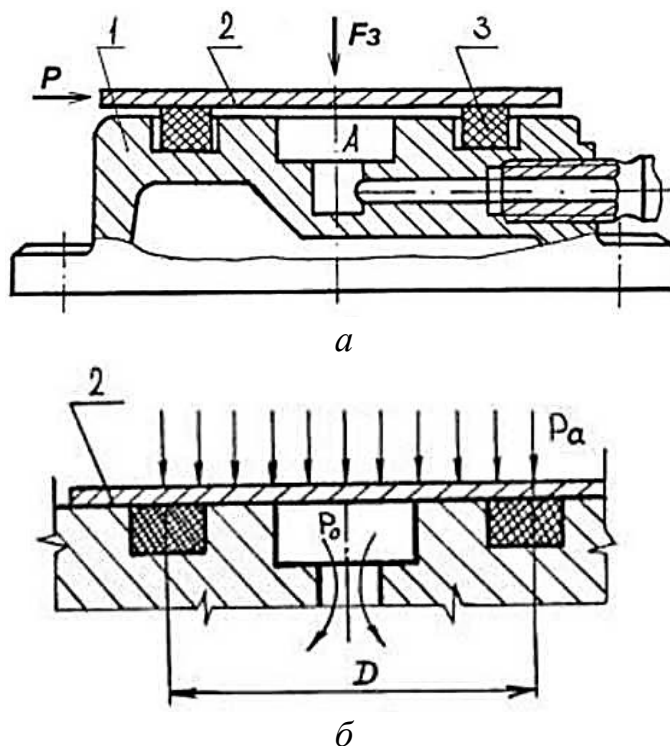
Схема вакуумного привода приспособления с заготовкой в отжатом (а) и прижатом (б) состояниях
